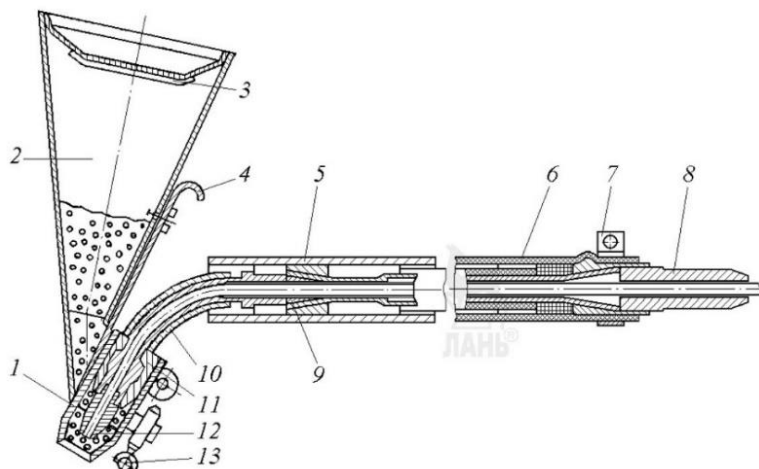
Горелка шлангового полуавтомата для сварки под флюсом
